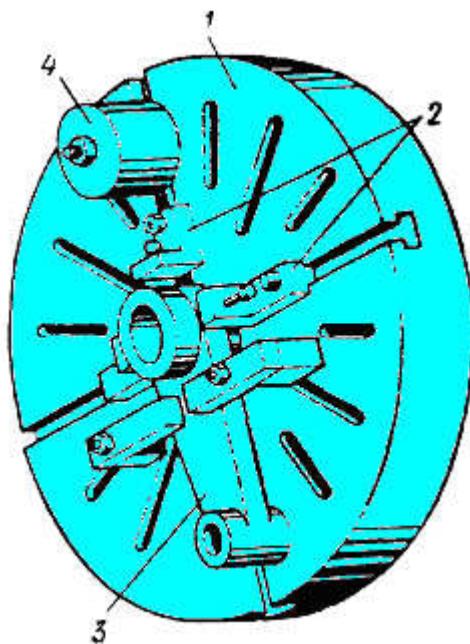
Установка и закрепление обрабатываемой детали на планшайбе
